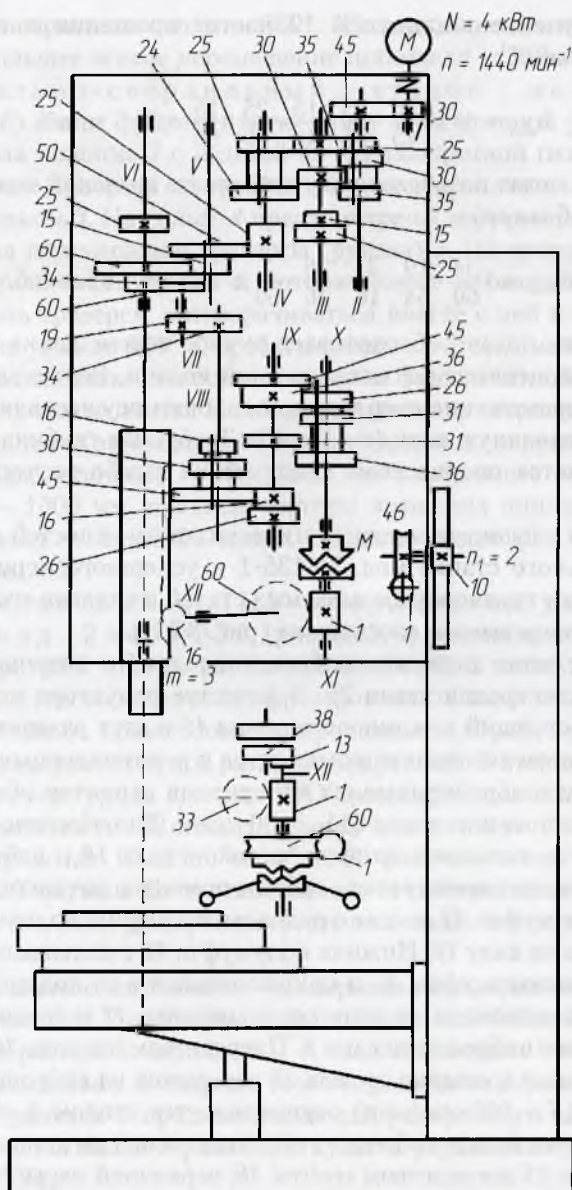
Кинематическая схема станка мод. 2Н135-1
